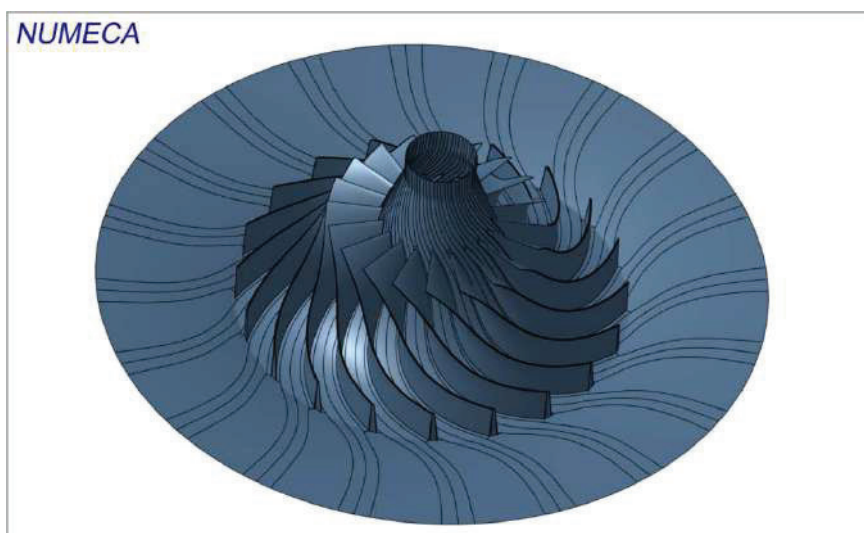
Большой масштабный центробежный компрессор (LSCC)
